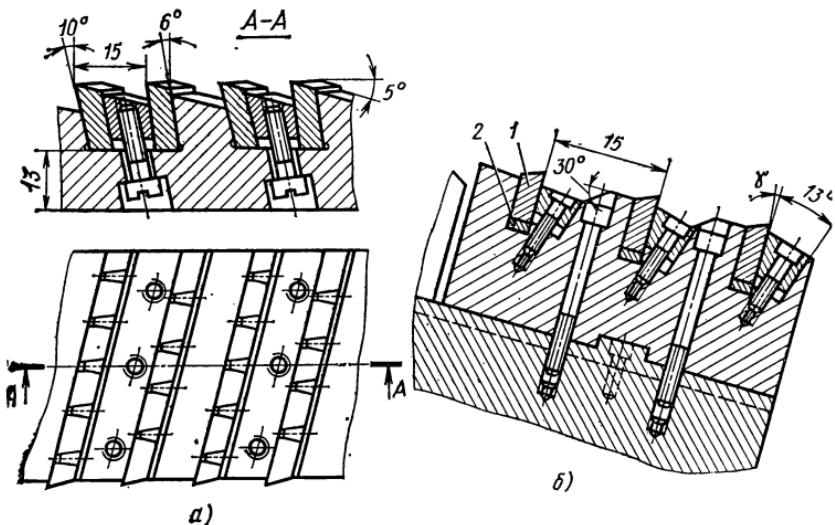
Схемы крепления твердосплавных пластин к корпусу протяжки:
